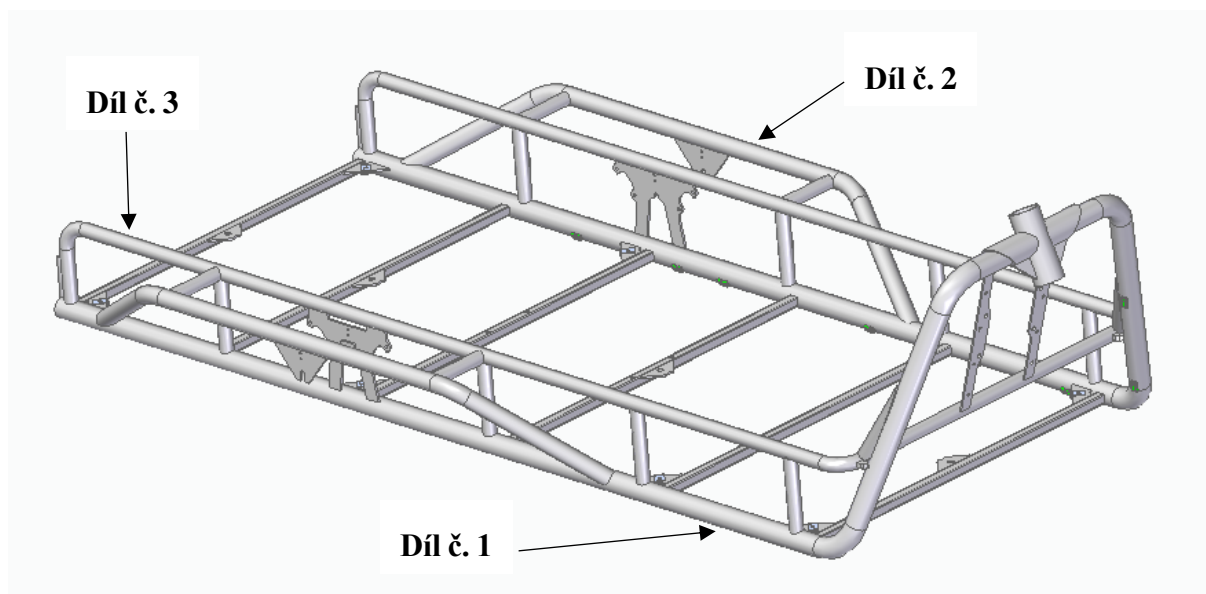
Svařenec výrobku 1 [Zdroj vlastní]
